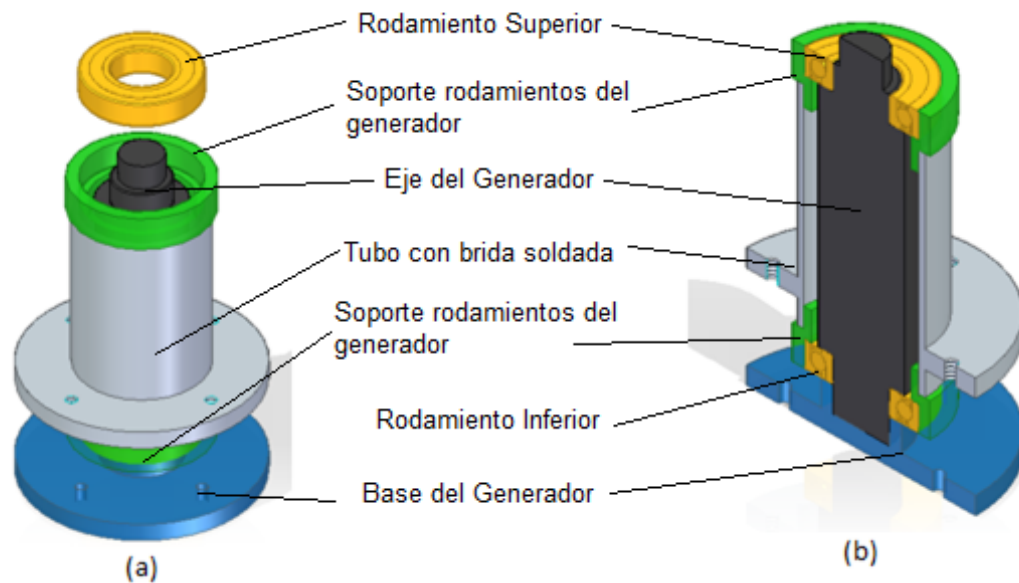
Acople del rodamiento superior de alineación. (a) Forma de ensamble del rodamiento superior. (b) Vista en corte isométrica del ensamble que se ha realizado.
